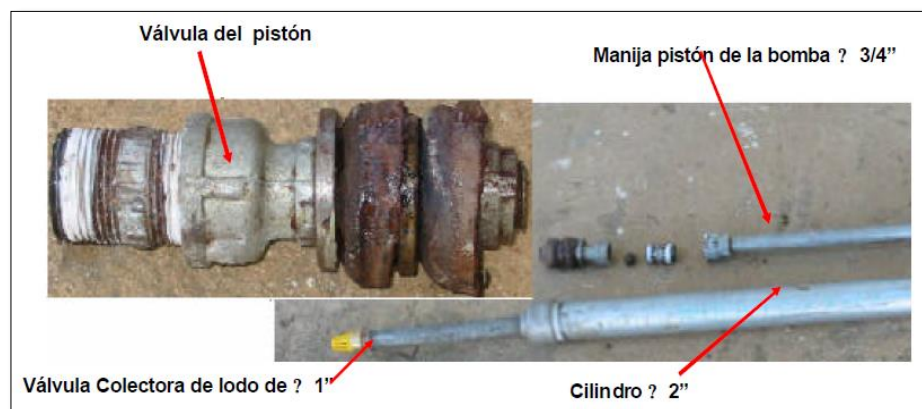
Detalles de las partes de la bomba tipo Bolivia.
